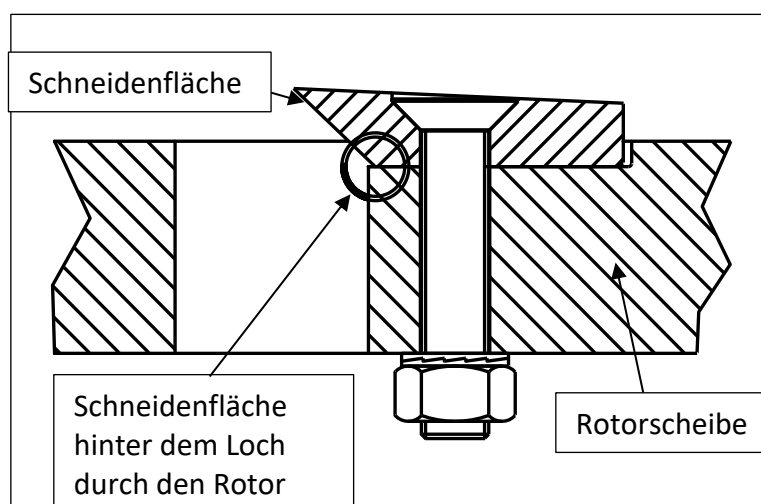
Die Schneidefläche des Messers befindet sich hinter der Kante des Lochs durch den Rotor
